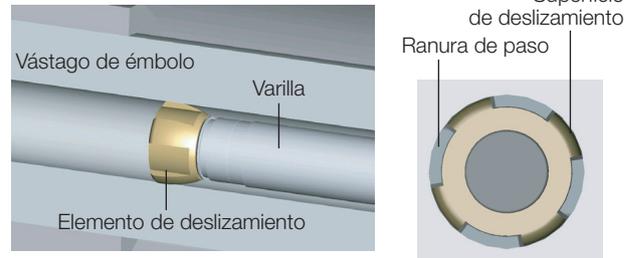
Vista detallada y vista desde arriba del elemento de deslizamiento
